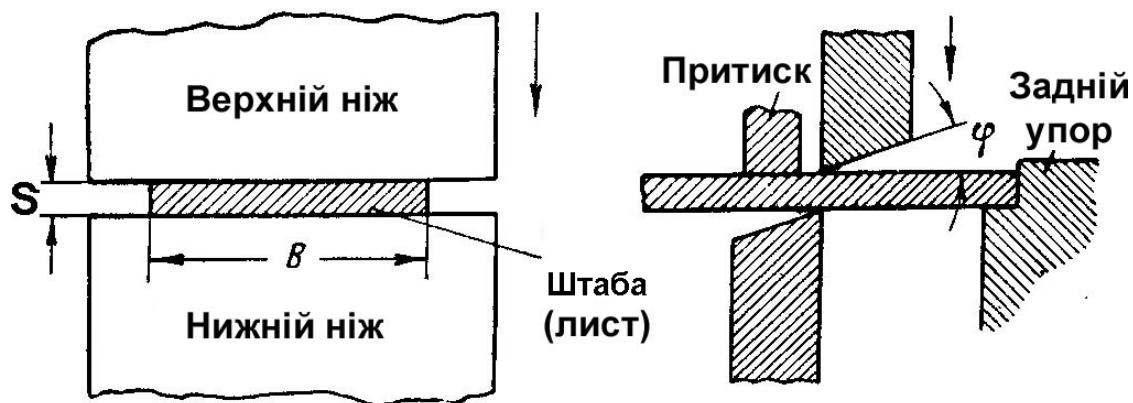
Схема різання ножицями з паралельними ножами
